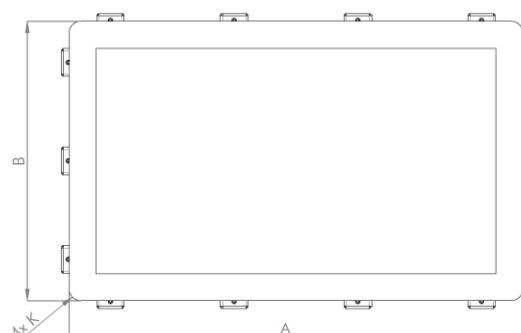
Dimensionen Open Frame Ausschnitt Front- und Distanzplatte
